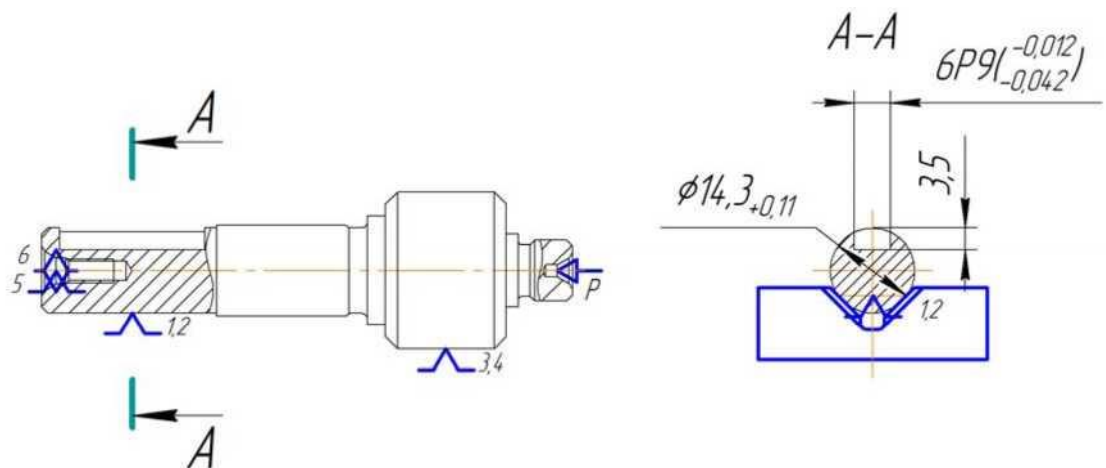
Схема базування деталі “Вал-шестерня”
